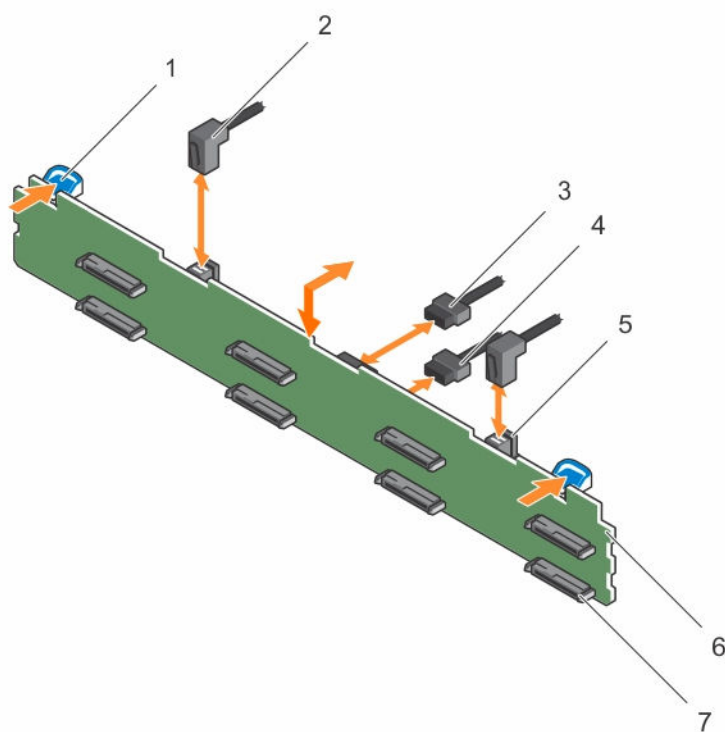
Extracción e instalación del plano posterior SAS/SATA (x8) de 3,5 pulgadas
